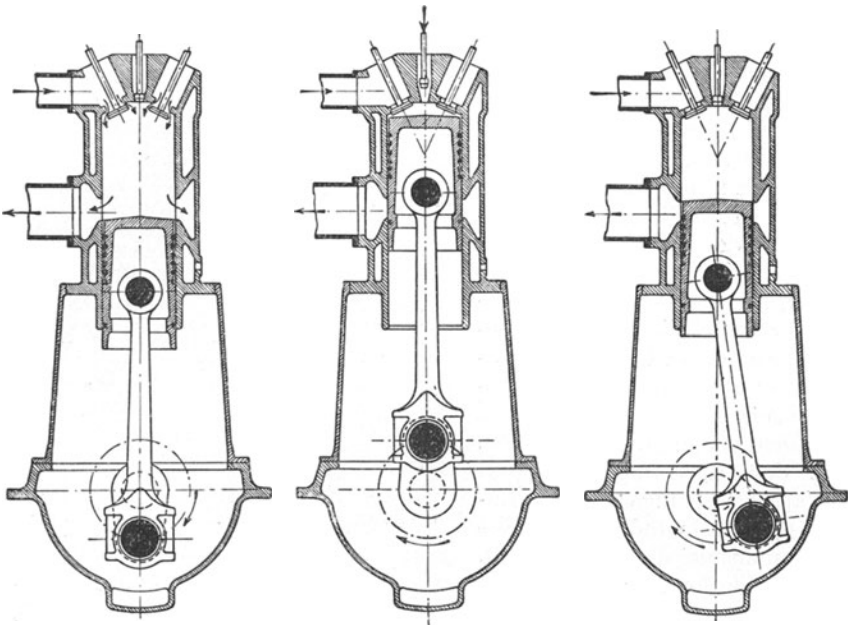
7. Hauptkolbenstellungen einer Zweitakt-Ölmaschine.
